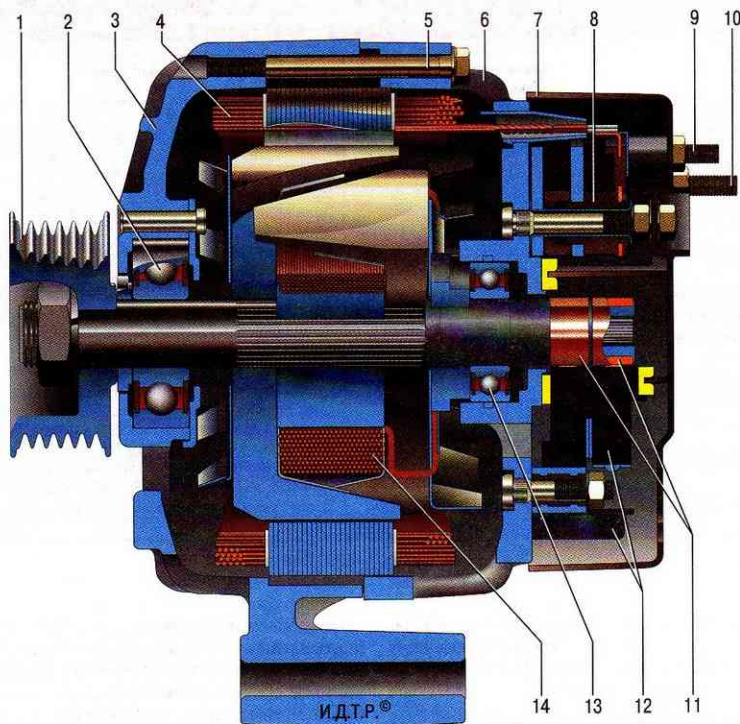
Генератор 5102.3771: 1 – шкив; 2 – передний подшипник; 3 – передняя крышка; 4 – статор; 5 – стяжной болт; 6 – задняя крышка; 7 – кожух; 8 – выпрямительный блок; 9 – вывод «D+» генератора; 10 – вывод «B+» генератора; 11 – контактные кольца ротора; 12 – регулятор напряжения со щеткодержателем; 13 – задний подшипник вала ротора; 14 – ротор
